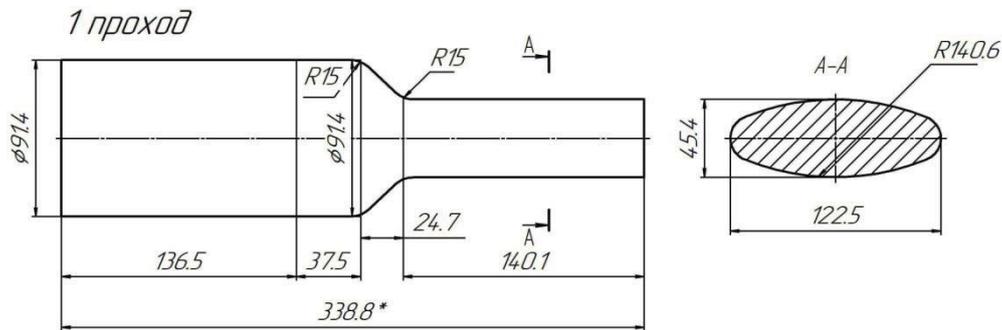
Эскиз заготовки после первого прохода вальцовки по схеме круг-овал
